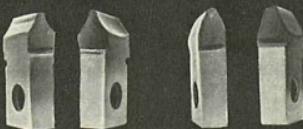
Червячные фрезы для нарезания цилиндрических шестерен с зацеплением М. Л. Новикова.
